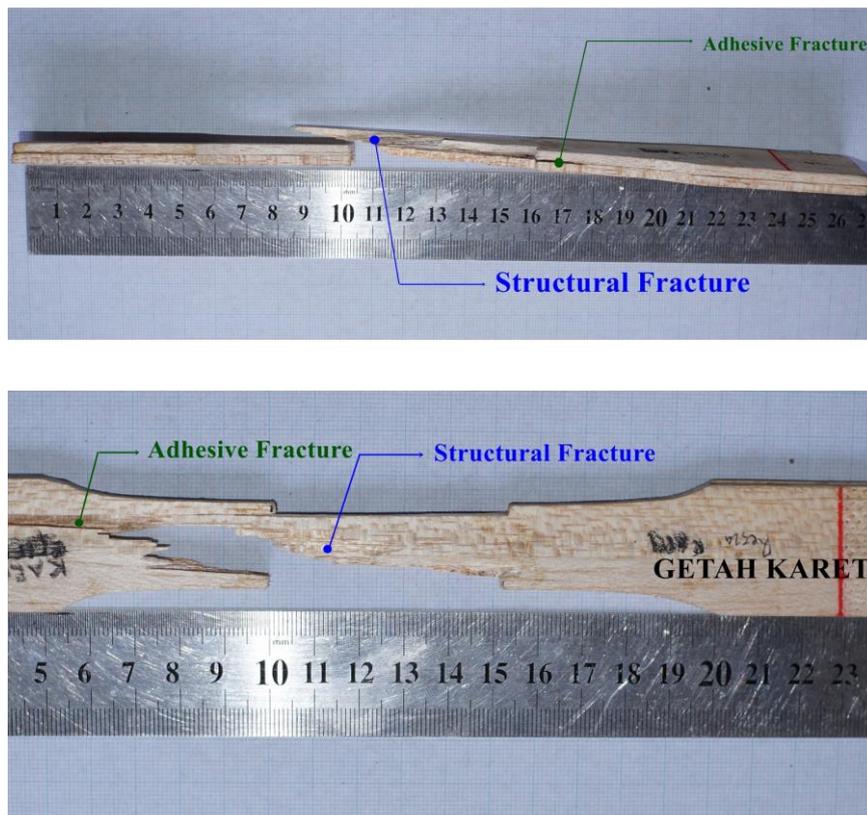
Foto patahan spesimen kayu balsa dengan *adhesive epoxy
